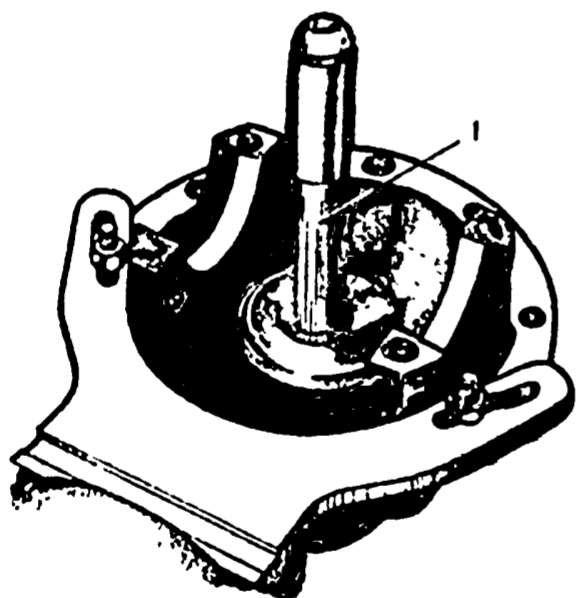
Установка с помощью оправки наружного кольца заднего подшипника ведущей шестерни: 1 - оправка А.70171
